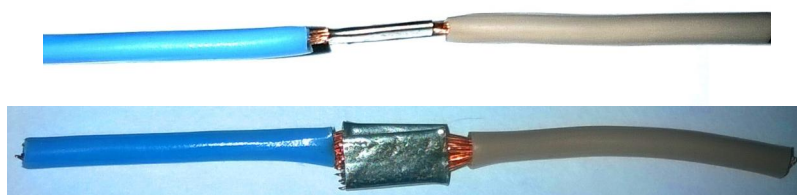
Сварное соединение с формующим элементом
